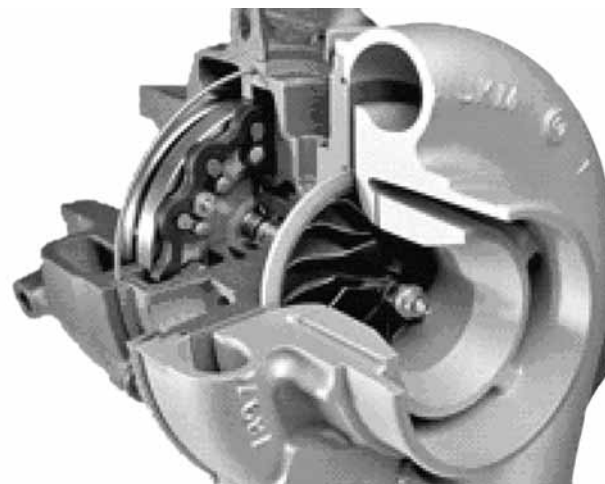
Один из вариантов привода лопаток соплового аппарата турбокомпрессора VNT DuteDrive
